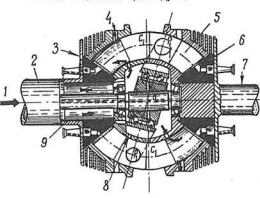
Продольный разрез двигателя 1 — впуск топливной; 2 — стационарный вал; 3 — ротор; 4 — выход отработавших газов; 5 — поршень; 6 — демонтирующаяся головка цилиндра; 7 — ведомый вал; 8 — впускное отверстие; 9 — уплотнение.
